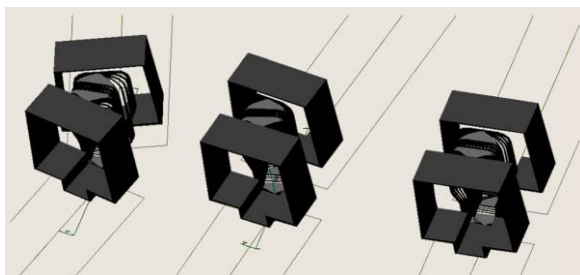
Межвагонный переход в подшипниковом соединении
